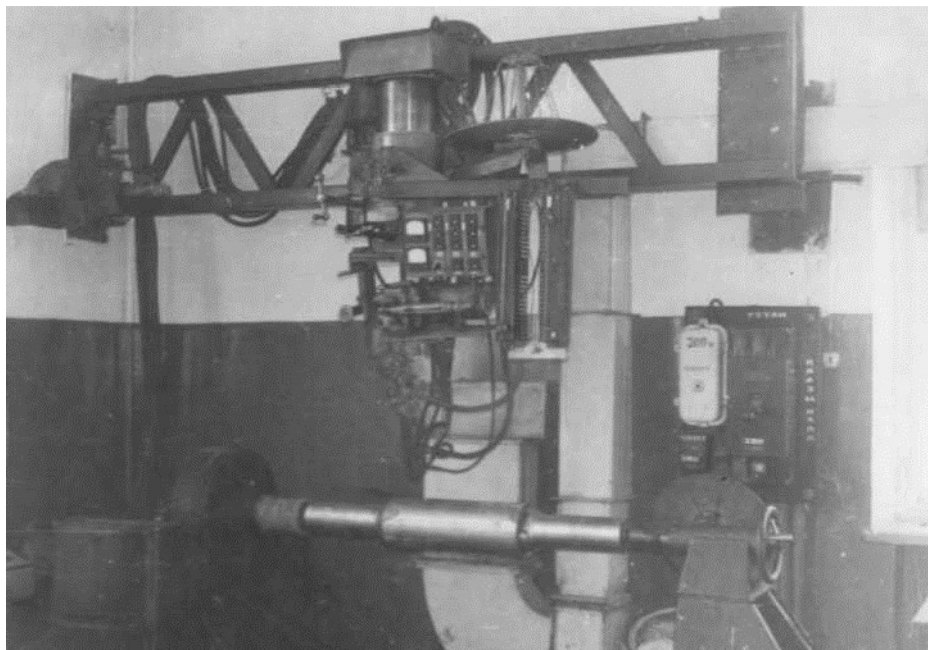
Общий вид установки для плазменной наплавки прокатных валков, разработанной в СибГИУ
